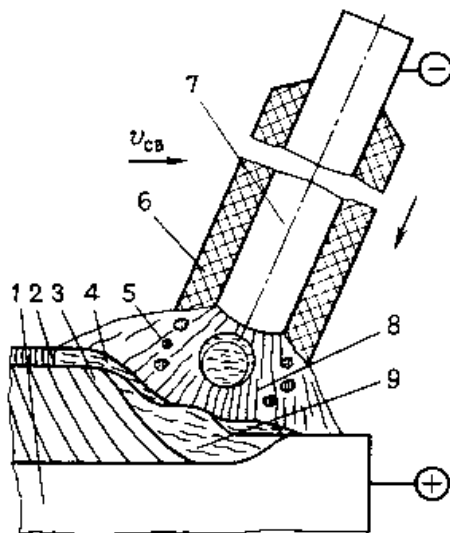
Схема процесса сварки металлическим покрытым электродом
